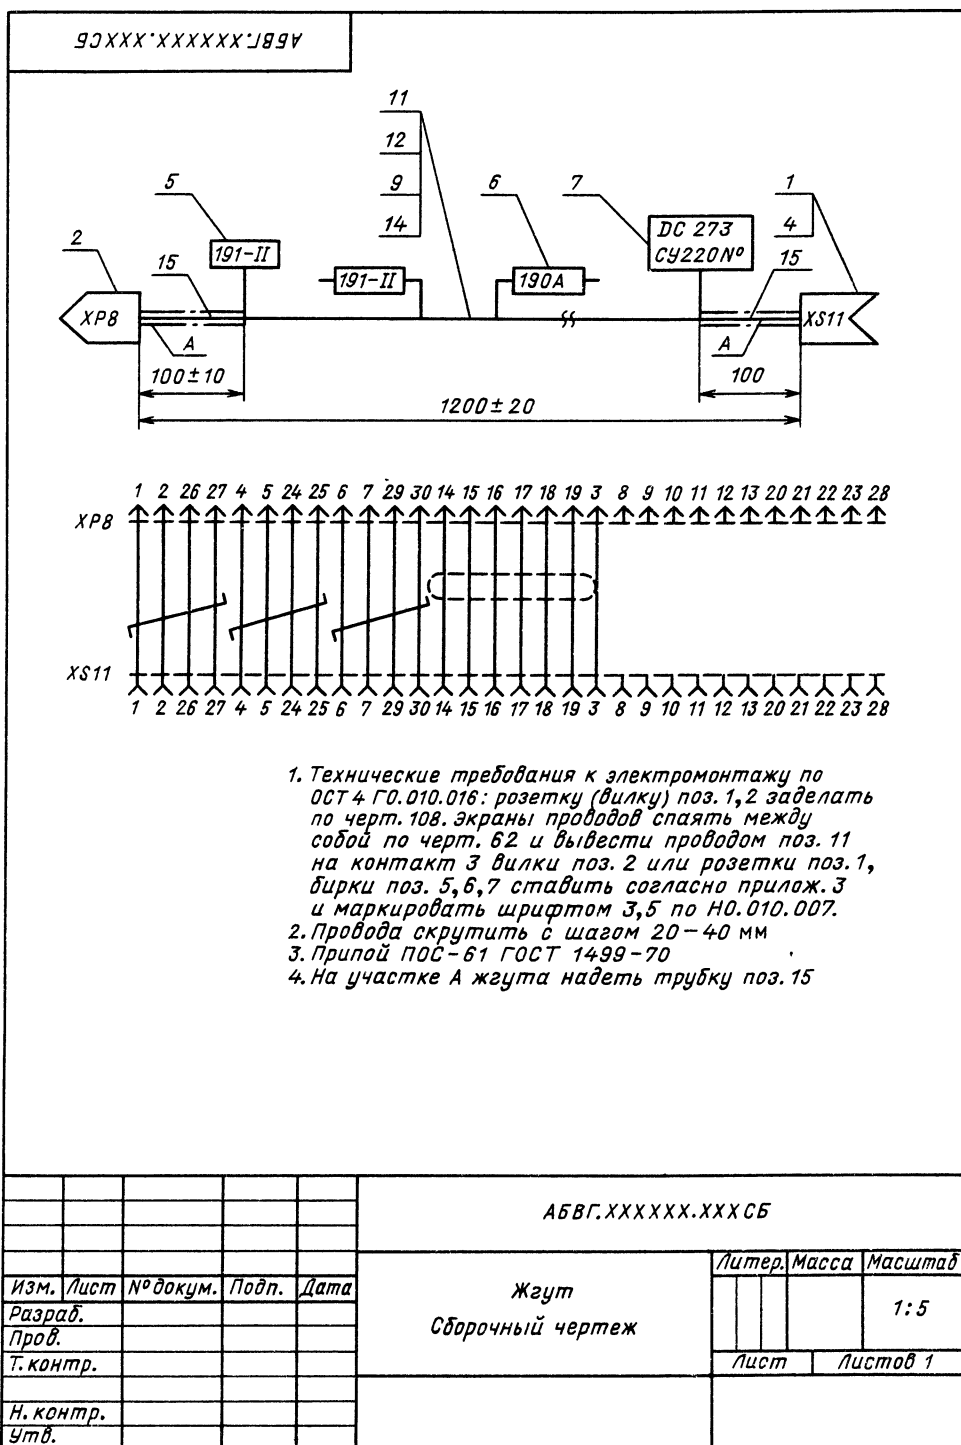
Сборочный чертеж жгута со схемой соединений
